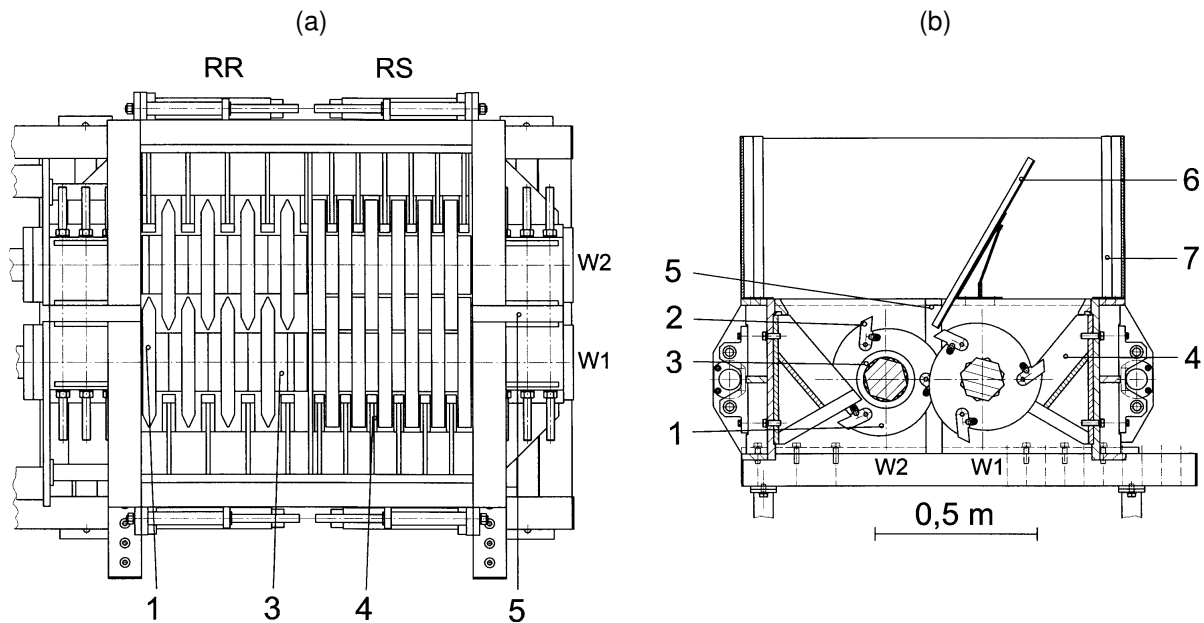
Aufbau der zweirotorigen Rotorschere (RS) und des zweirotorigen Rotorreißers (RR); (a) Draufsicht (ohne Aufgabeschurre und Schutzgehäuse); (b) Seitenansicht der Rotorschere
